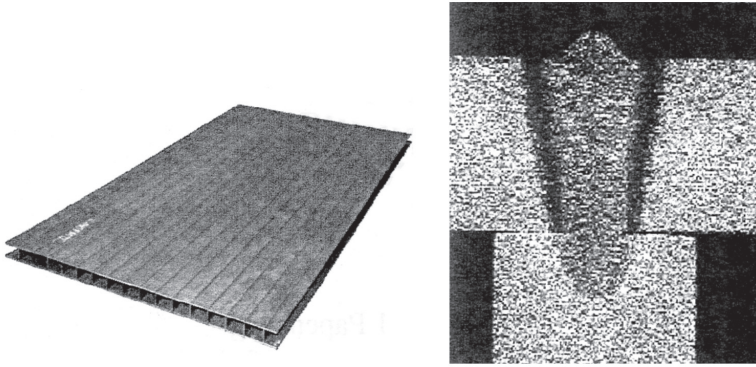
Многослойная панель, полученная при помощи лазерной сварки
